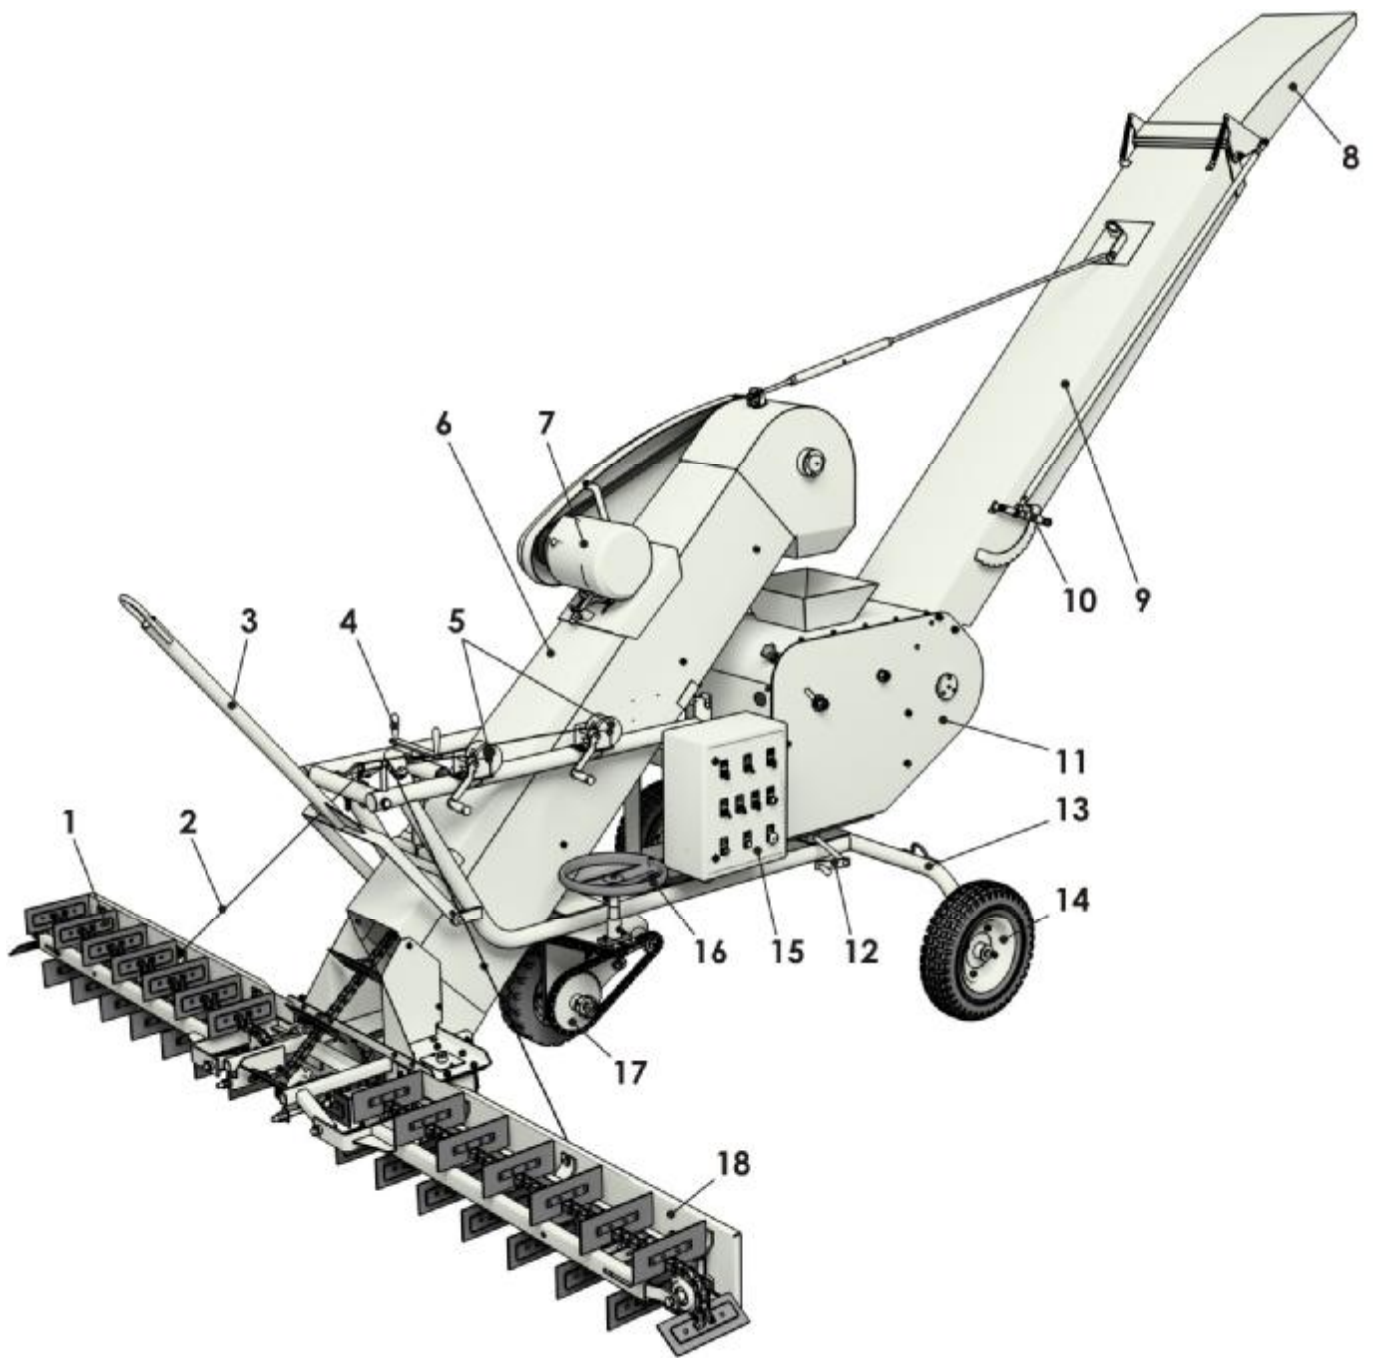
Общий вид метателя зерна МЗС-90-20-01М
